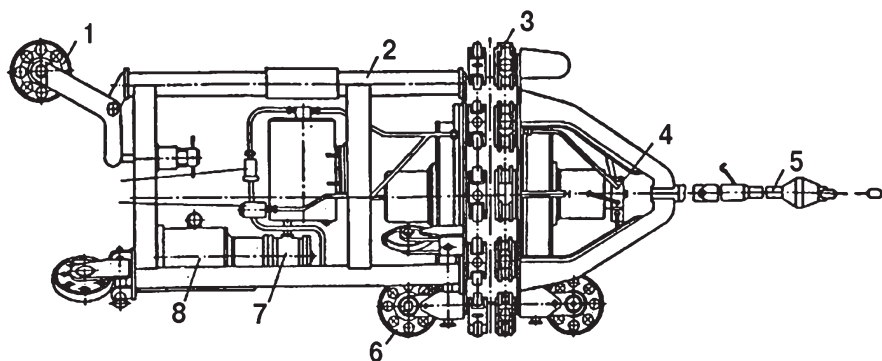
Общий вид внутреннего центриатора ЦВ-102:
